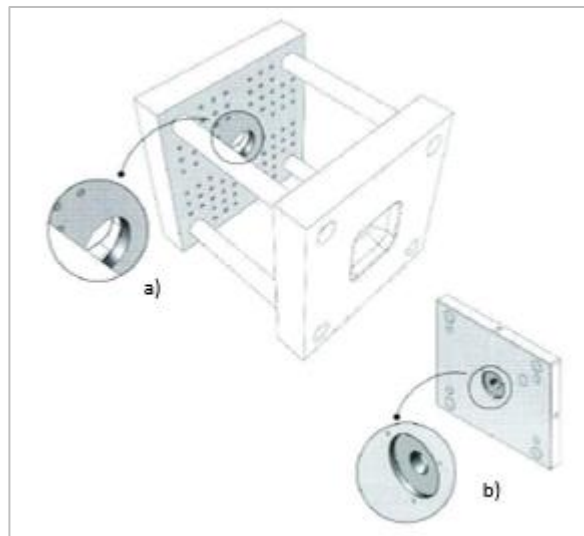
Zona de ajuste da anilha de centragem: a) Prato da máquina de injeção; b) Placas do molde [2].
